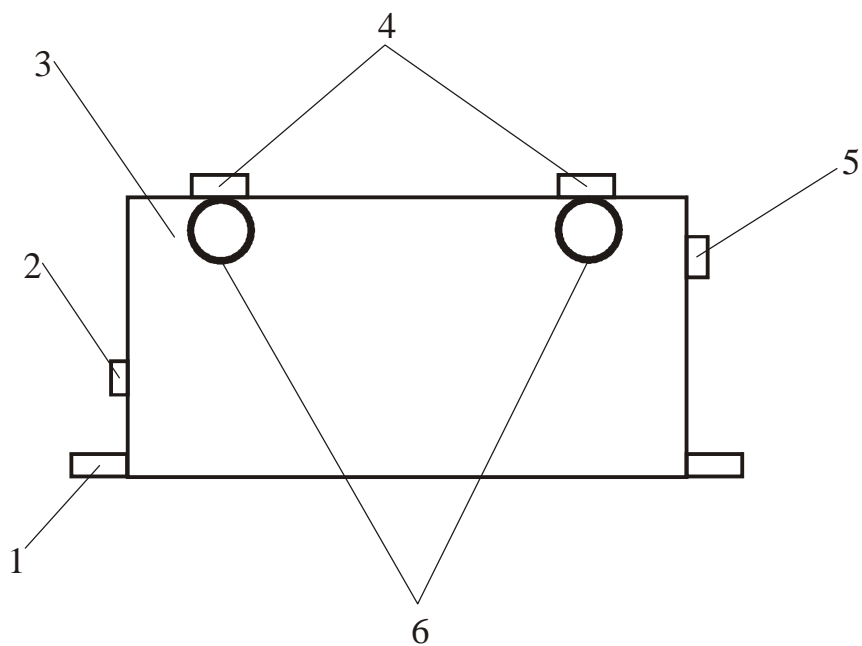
Блок измерения и усиления (вид сбоку): 1— крепления корпуса; 2— кнопка включения; 3— корпус; 4— датчики веса; 5— выходной разъем аналогового сигнала; 6— подвесы
